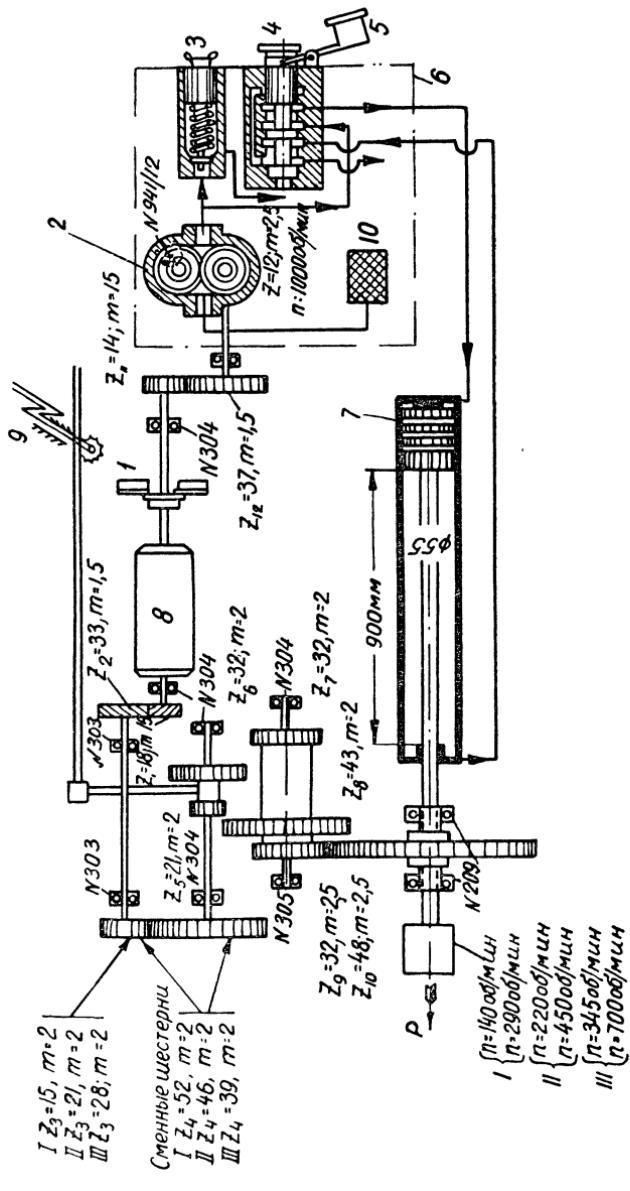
Кинематическая и гидравлическая схема электросверла ЭСГП-4:
